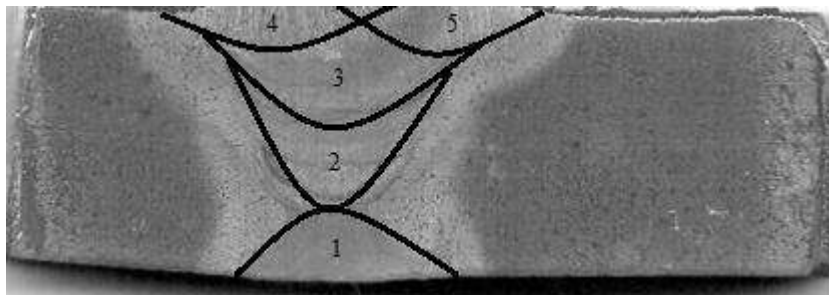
Secuencia de aplicación de los cordones de soldadura.
